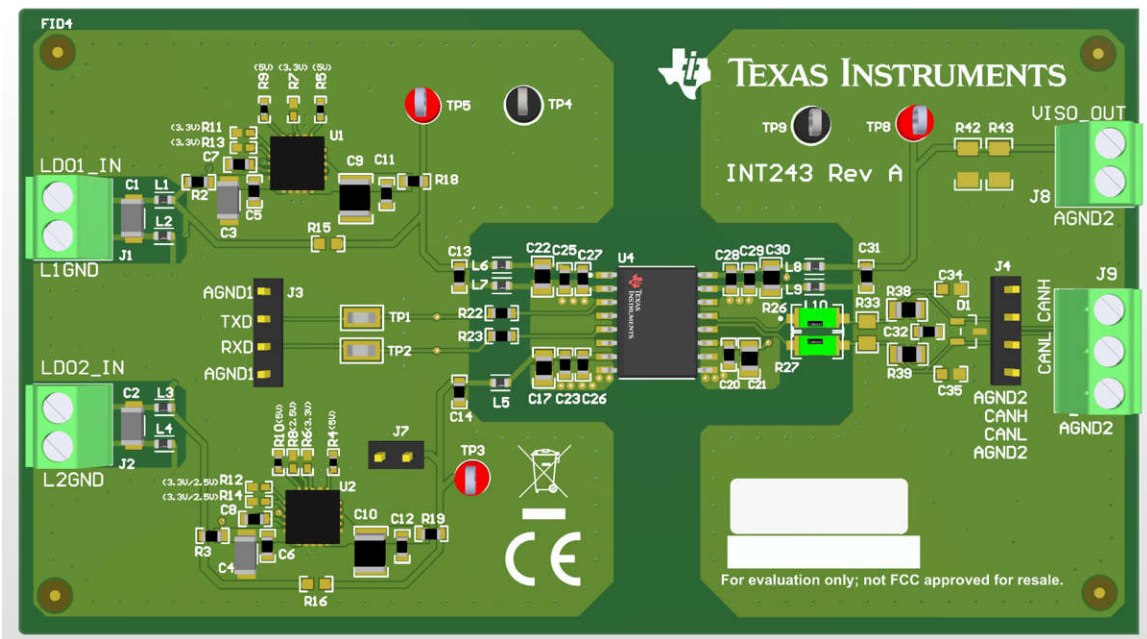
ISOW1050DWEEVM PCB 3D 视图 - 顶层
